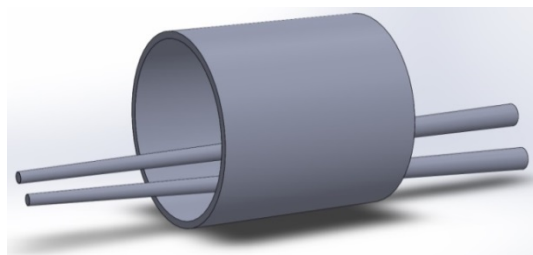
Два длинномера в корпусе корообдирочного барабана
